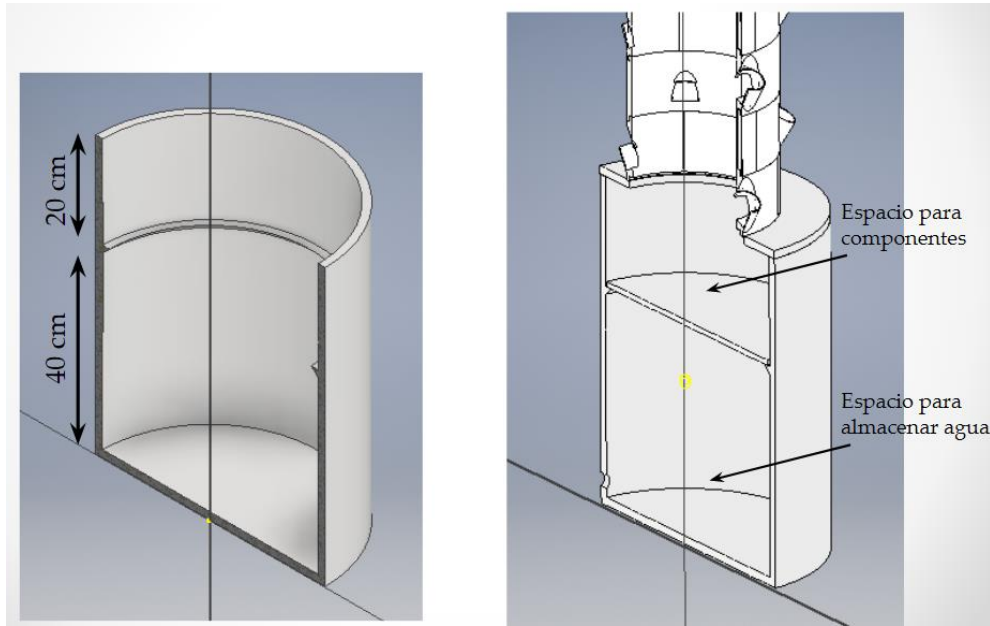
Vista en corte de la base de la torre de piezas acoplables.
